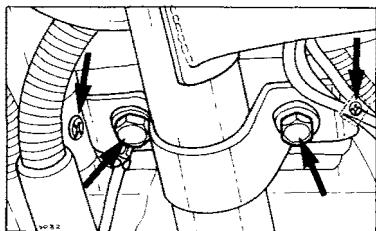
Болты и винты верхнего крепежа рулевой колонки
